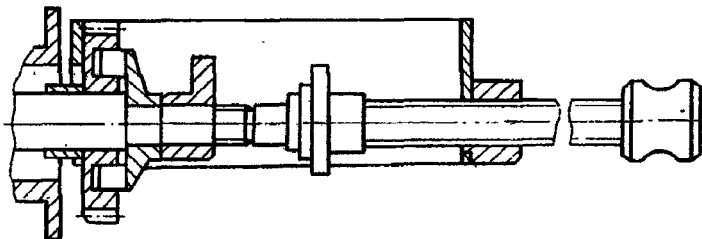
Снятие эксцентрика и ведущего зубчатого колеса с кулачкового вала ТНВД
